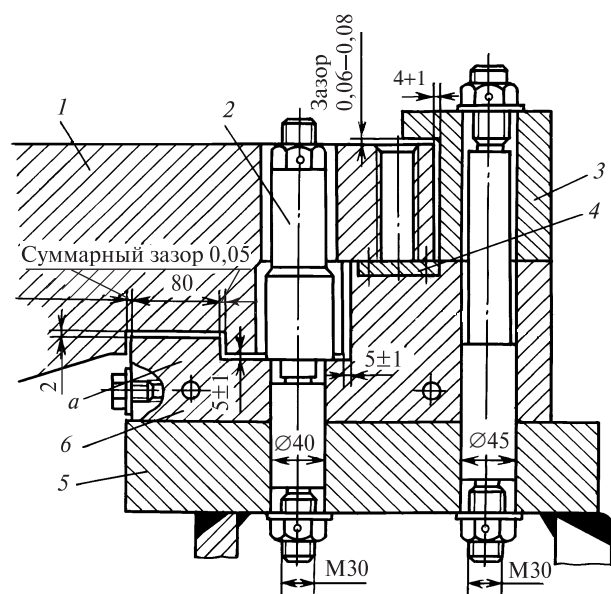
Узел сопряжения лапы и корпуса подшипника в турбине Т-250/300-23,5 ТМЗ
